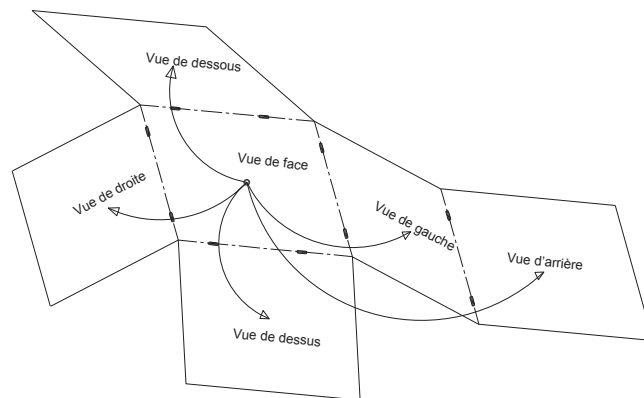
Dépliage des 6 faces du cube selon les charnières liant chaque vue
